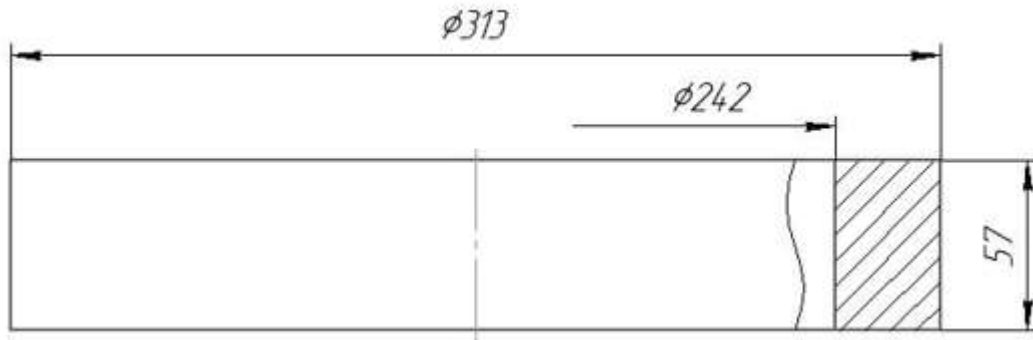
Ескіз поковки для виготовлення кільця
